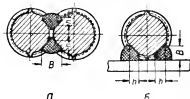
Схема измеряемых размеров сварных фланговых швов:
